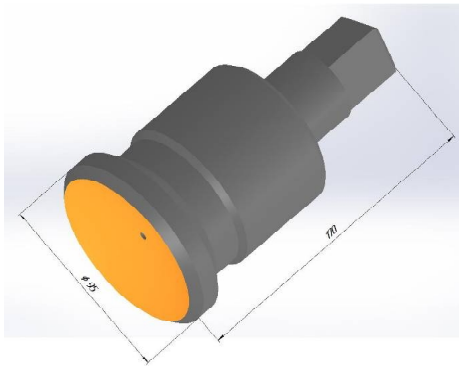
Деталь «Упор» (жёлтым цветом обозначена упрочняемая поверхность)
